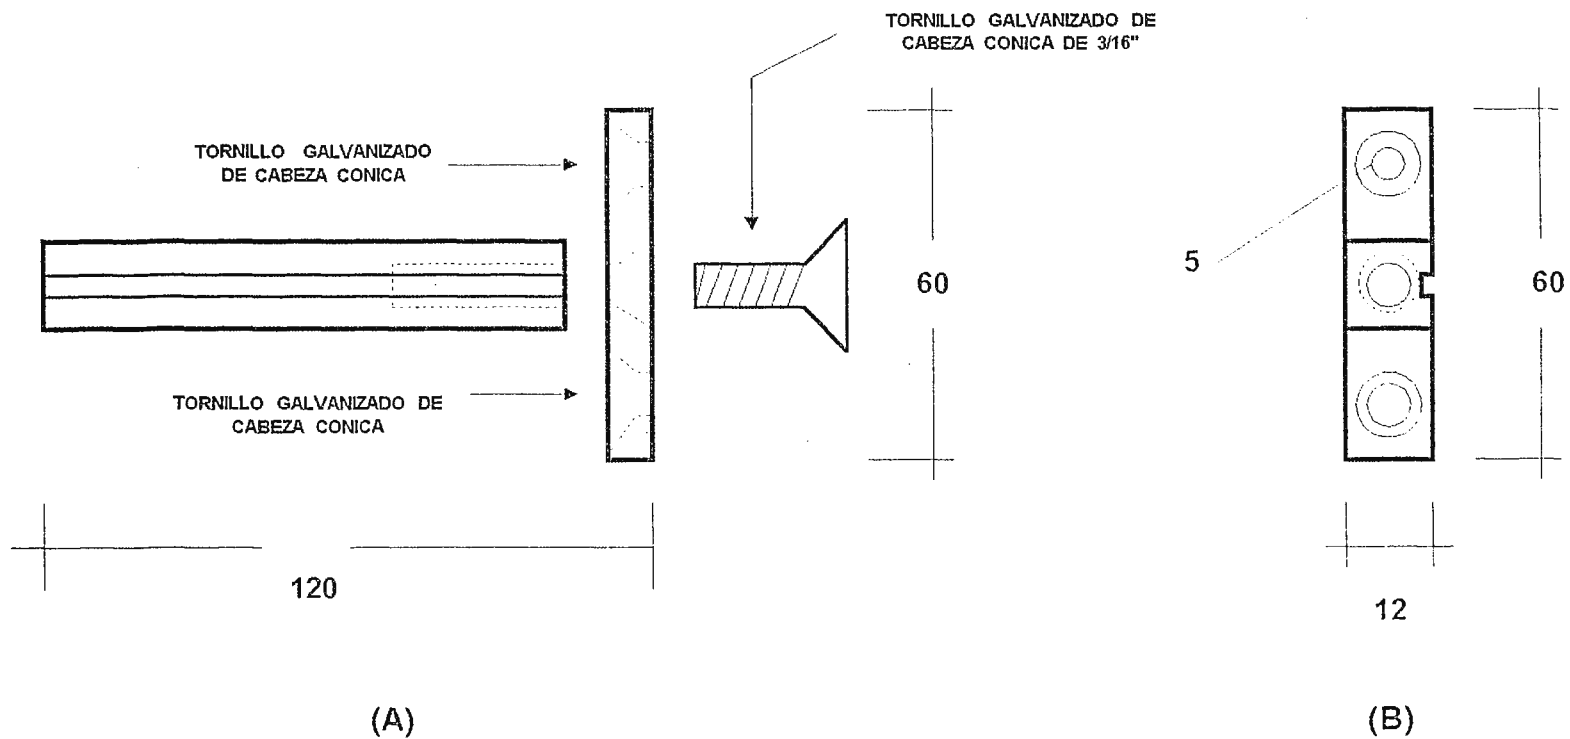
PIEZA DE SOPORTE DE TARJETAS ELECTRONICAS EN EL TABLERO DE ELEMENTOS , (A) VISTA LATERAL; (B) VISTA FRONTAL.
